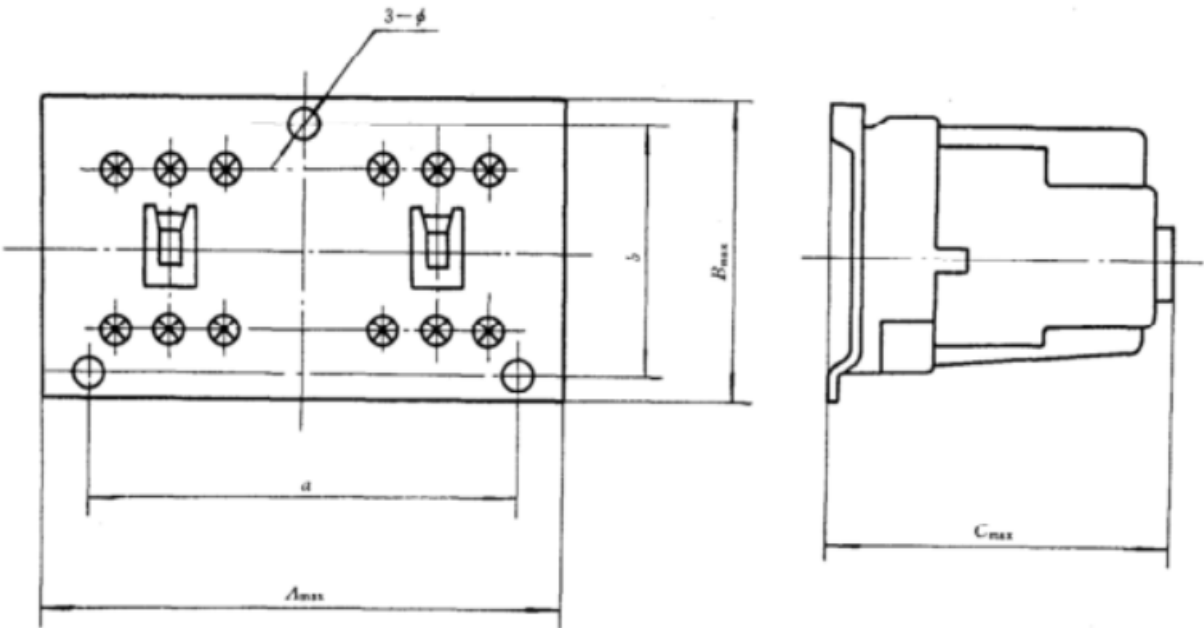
CJX5-16/N~105/N 型联锁接触器外形尺寸与安装尺寸
